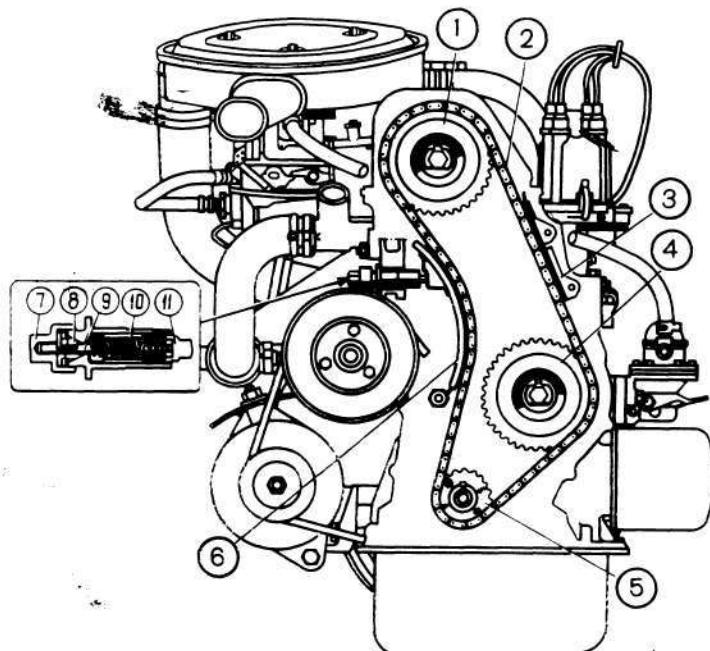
Схема привода механизма газораспределения: 1 — звездочка распределительного вала; 2 — цепь; 3 — успокоитель; 4 — звездочка привода масляного насоса; 5 — звездочка коленчатого вала; 6 — балансирный вал; 7 — фиксирующая гайка стержня натяжителя; 8 — зажимной сухарь; 9 — регулировочный стержень натяжителя; 10 — пружина плунжера; 11 — плунжер натяжителя
